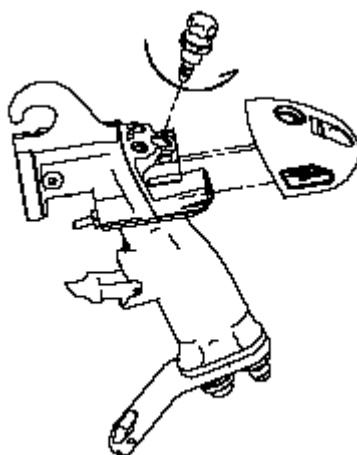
Montaż korpusu pistoletu / uchwytu
